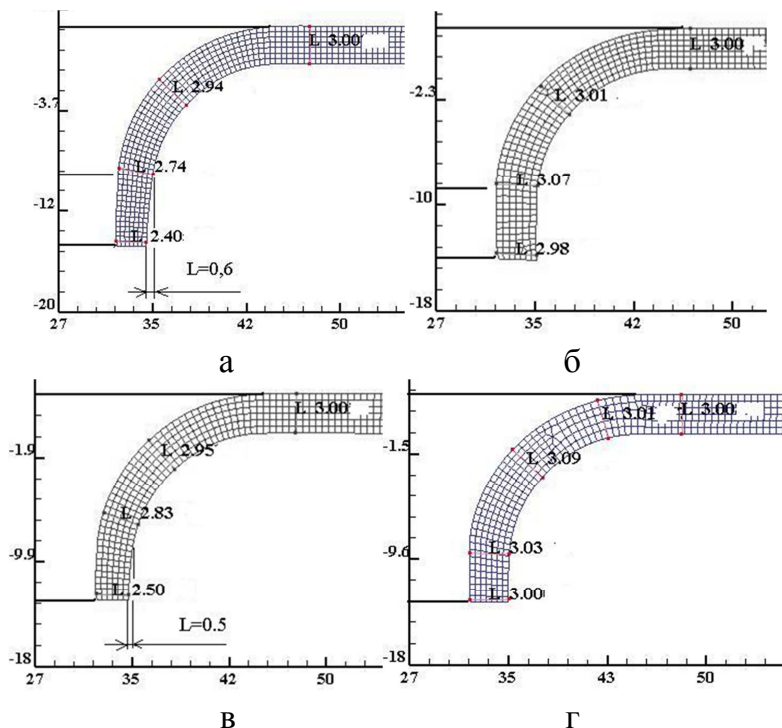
Розміри L в міліметрах zdeформованих частин заготовок, які отримані відбортуванням традиційної заготовки (а, в) та зпрофільованої заготовки (б, г) з коефіцієнтами відбортування 0,65 і 0,7)
